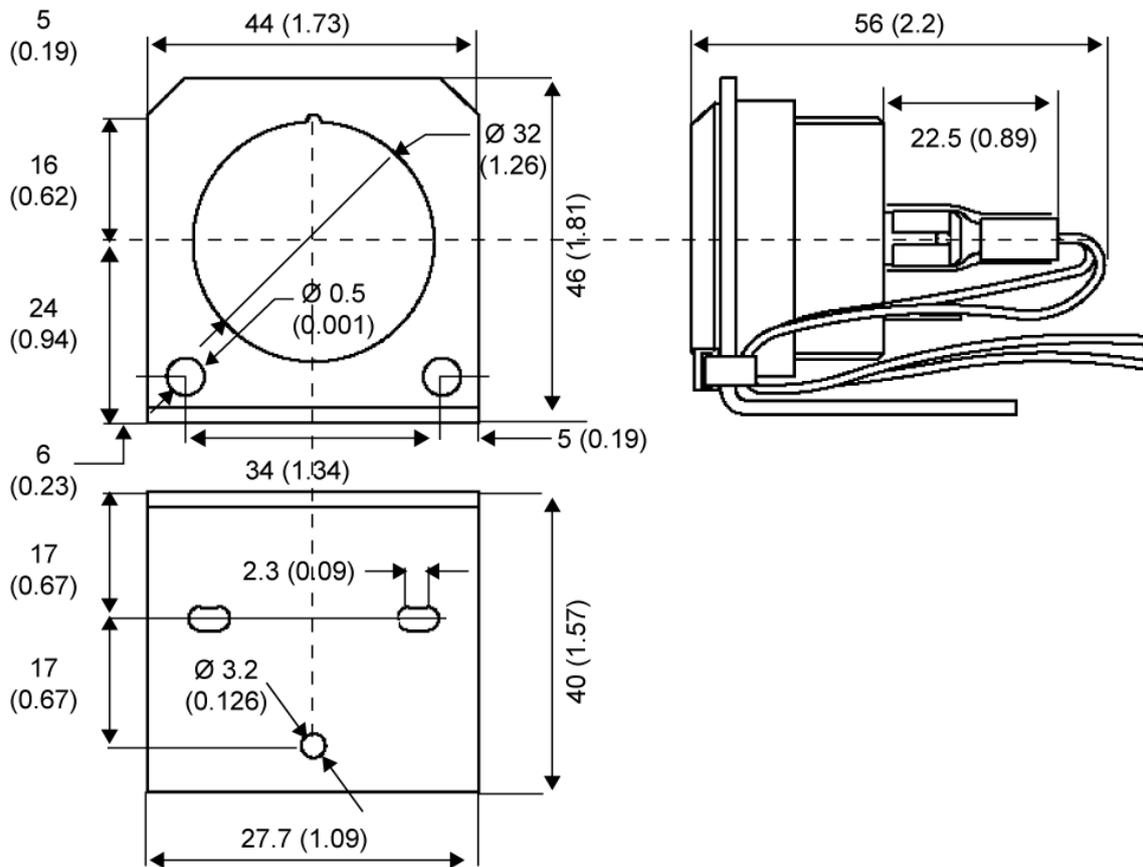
Размеры РЭ-100 и шаблон для сверления
